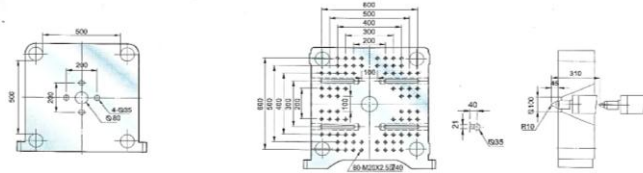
Dimensi *Mold Platen* untuk mesin injeksi merk HWA CHIN MACHINERY FACTORY bagian 1
